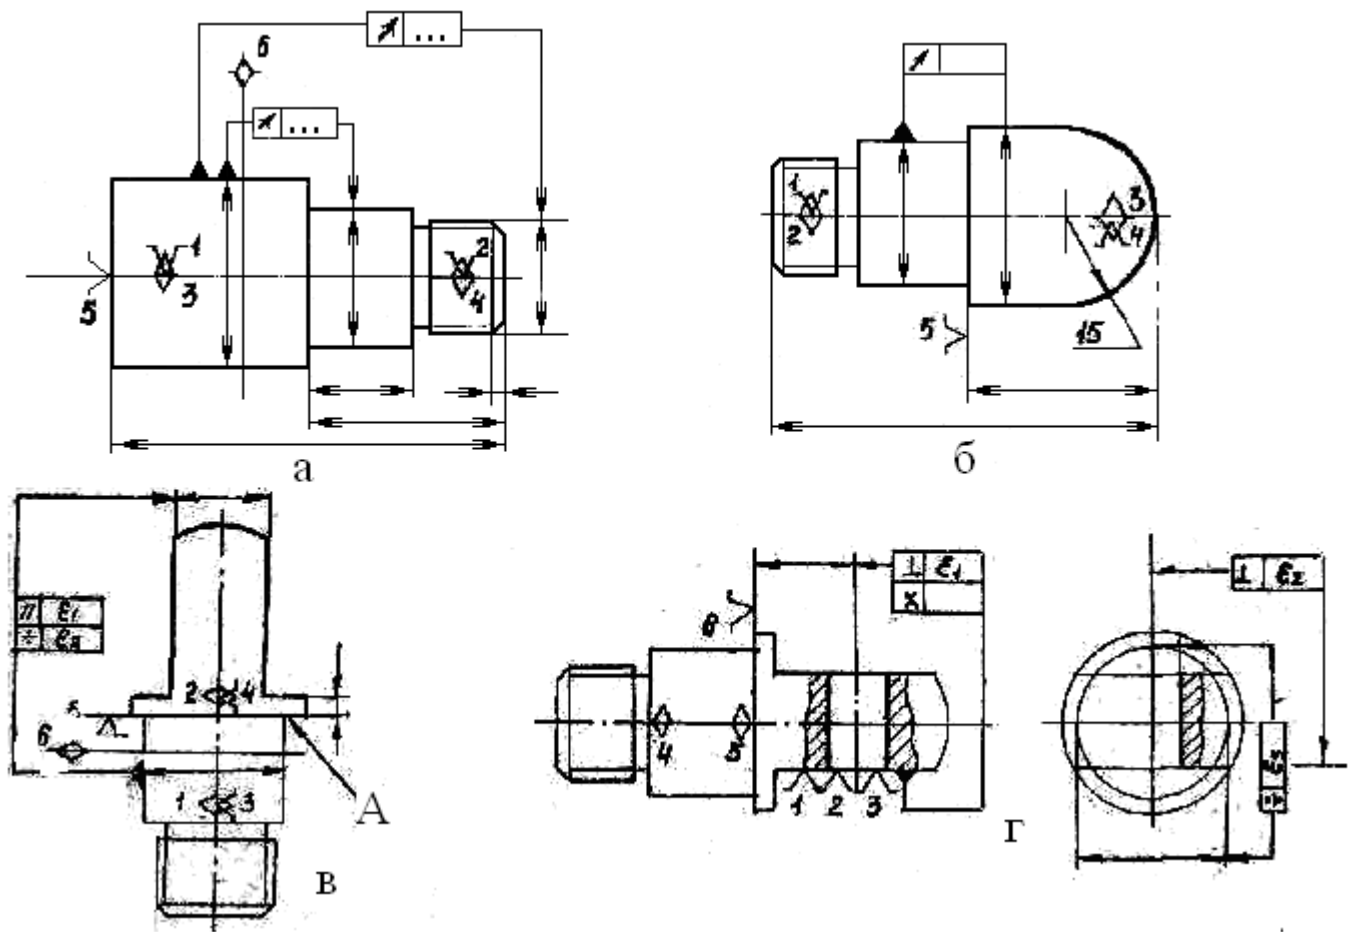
Чертеж детали с размерной связью ее рабочих поверхностей
